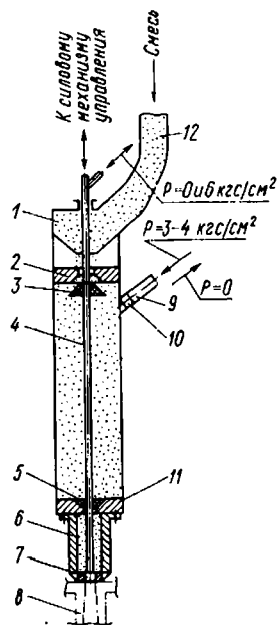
Пескодувная головка фирмы «А. Hottinger»: 1 — корпус; 2 и 11 — перегородки; 3, 5 и 10 — клапаны; 4 — шток; 6 — насадка; 7 — вдувное отверстие; 8 — кокиль; 9 — патрубок; 12 — труба для смеси
